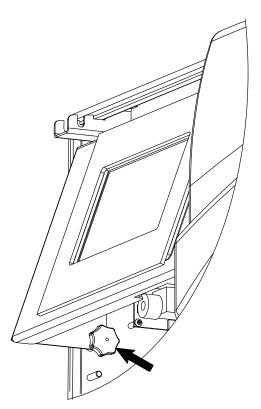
Position der Schrauben der Touchscreen-Baugruppe
